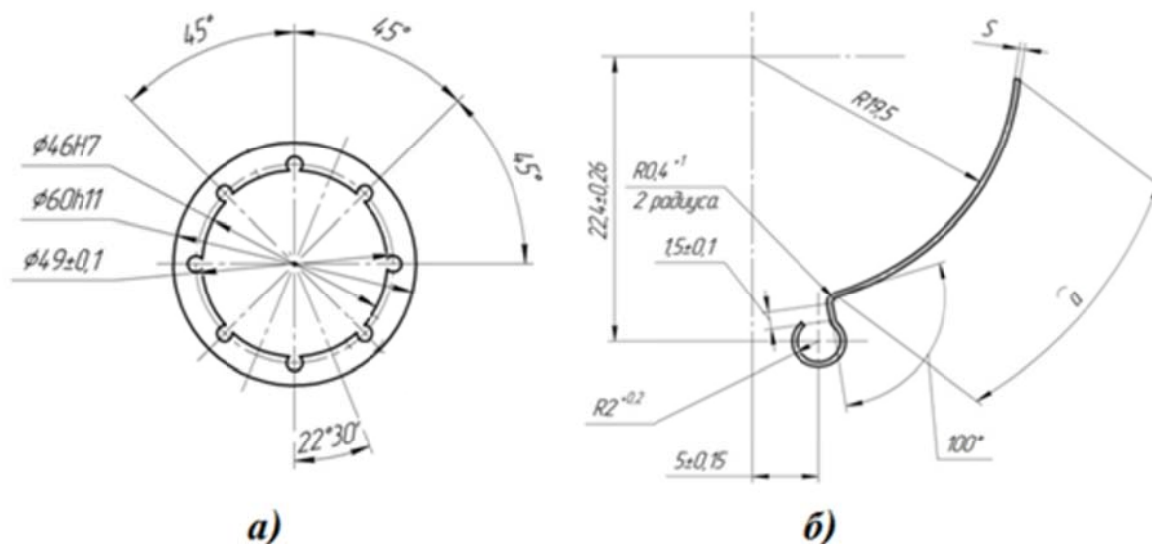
Элементы конструкции лепесткового подшипника:
